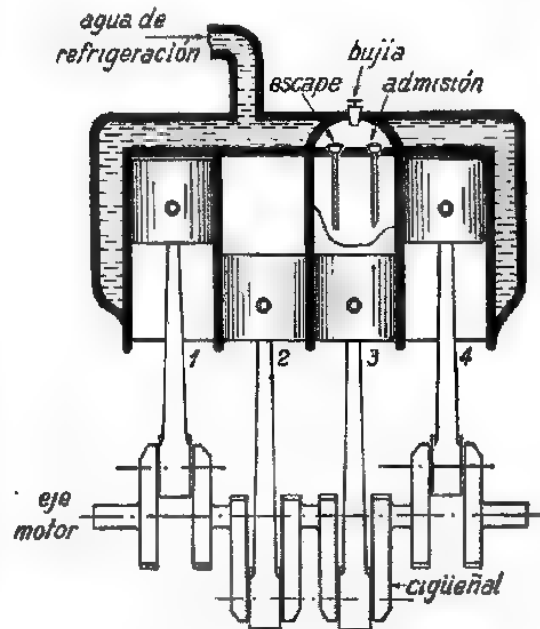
Corte longitudinal de un motor a explosión policilíndrico.
